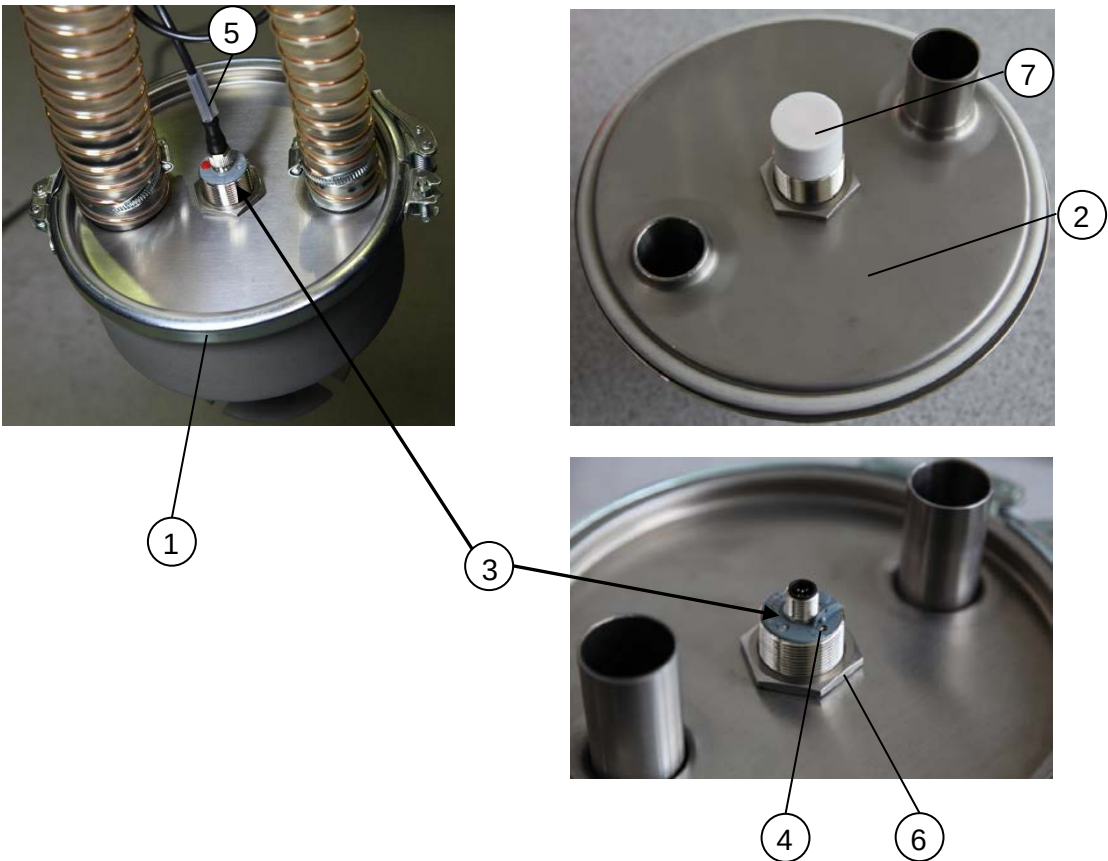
Montage/remplacement du capteur de niveau dans la trémie de la machine
